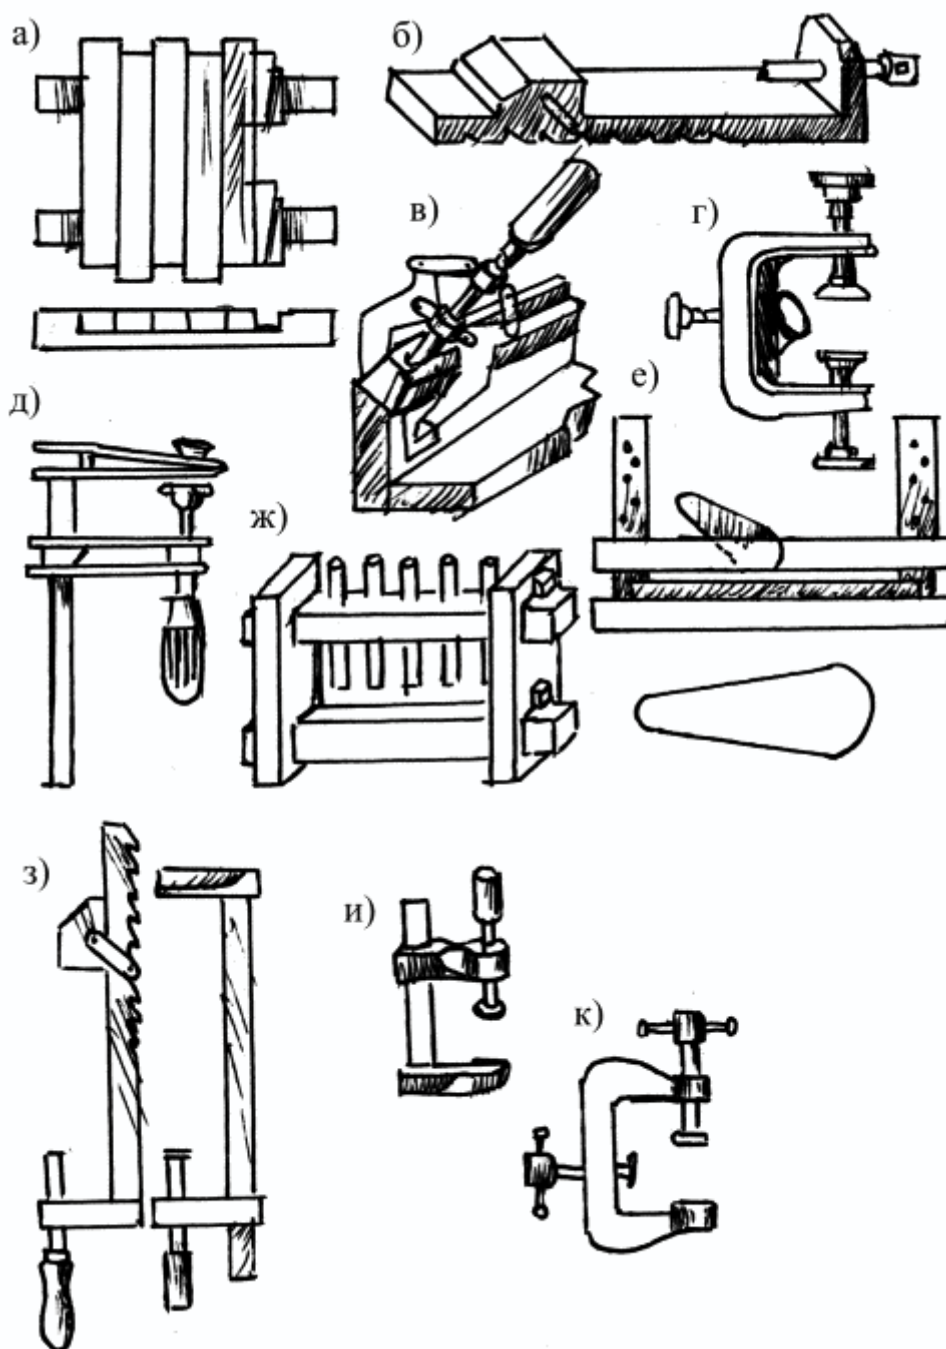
Приспособления и инструменты для склеивания деталей: а – пресс с хомутовыми струбцинами; б – пресс на стяжных болтах; в – пресс с деревянными клиньями; г, д, е, ж, з, и, к – струбцины для коротких и длинных деталей
